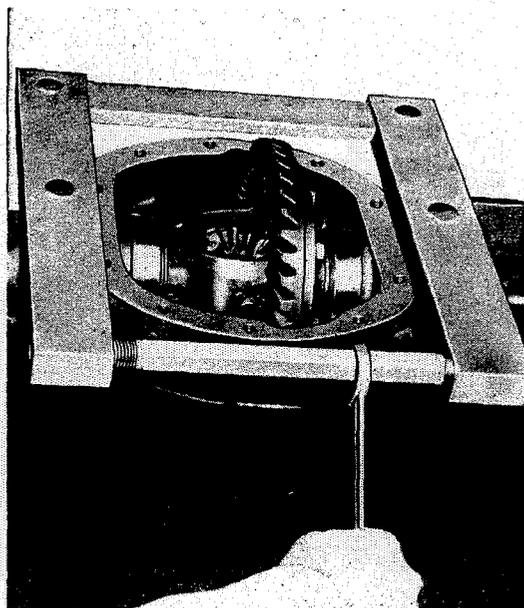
Spreizwerkzeug für Hinterachsgehäuse
